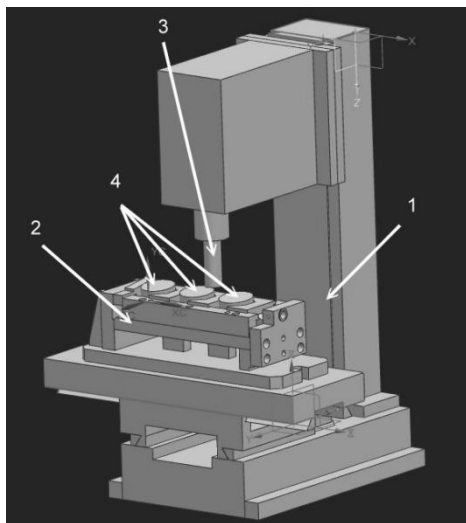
Сборная модель технологической системы. 1 — станок, 2 — приспособление, 3 — инструмент, 4 — заготовки
